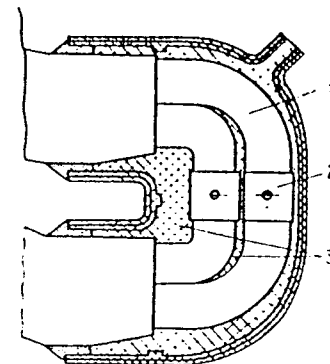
Соединение стержней обмотки статора: 1 — головки стержней; 2 — хомутики; 3 — прессованные коробки
